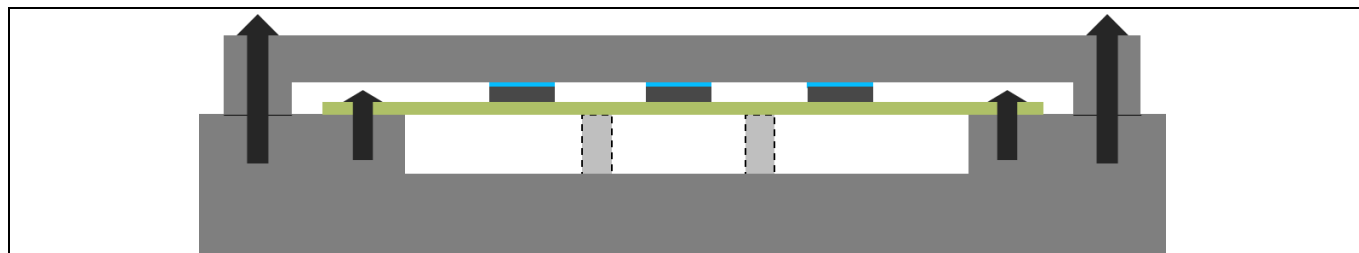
PCB 下方的额外支座可防止 PCB 弯曲
